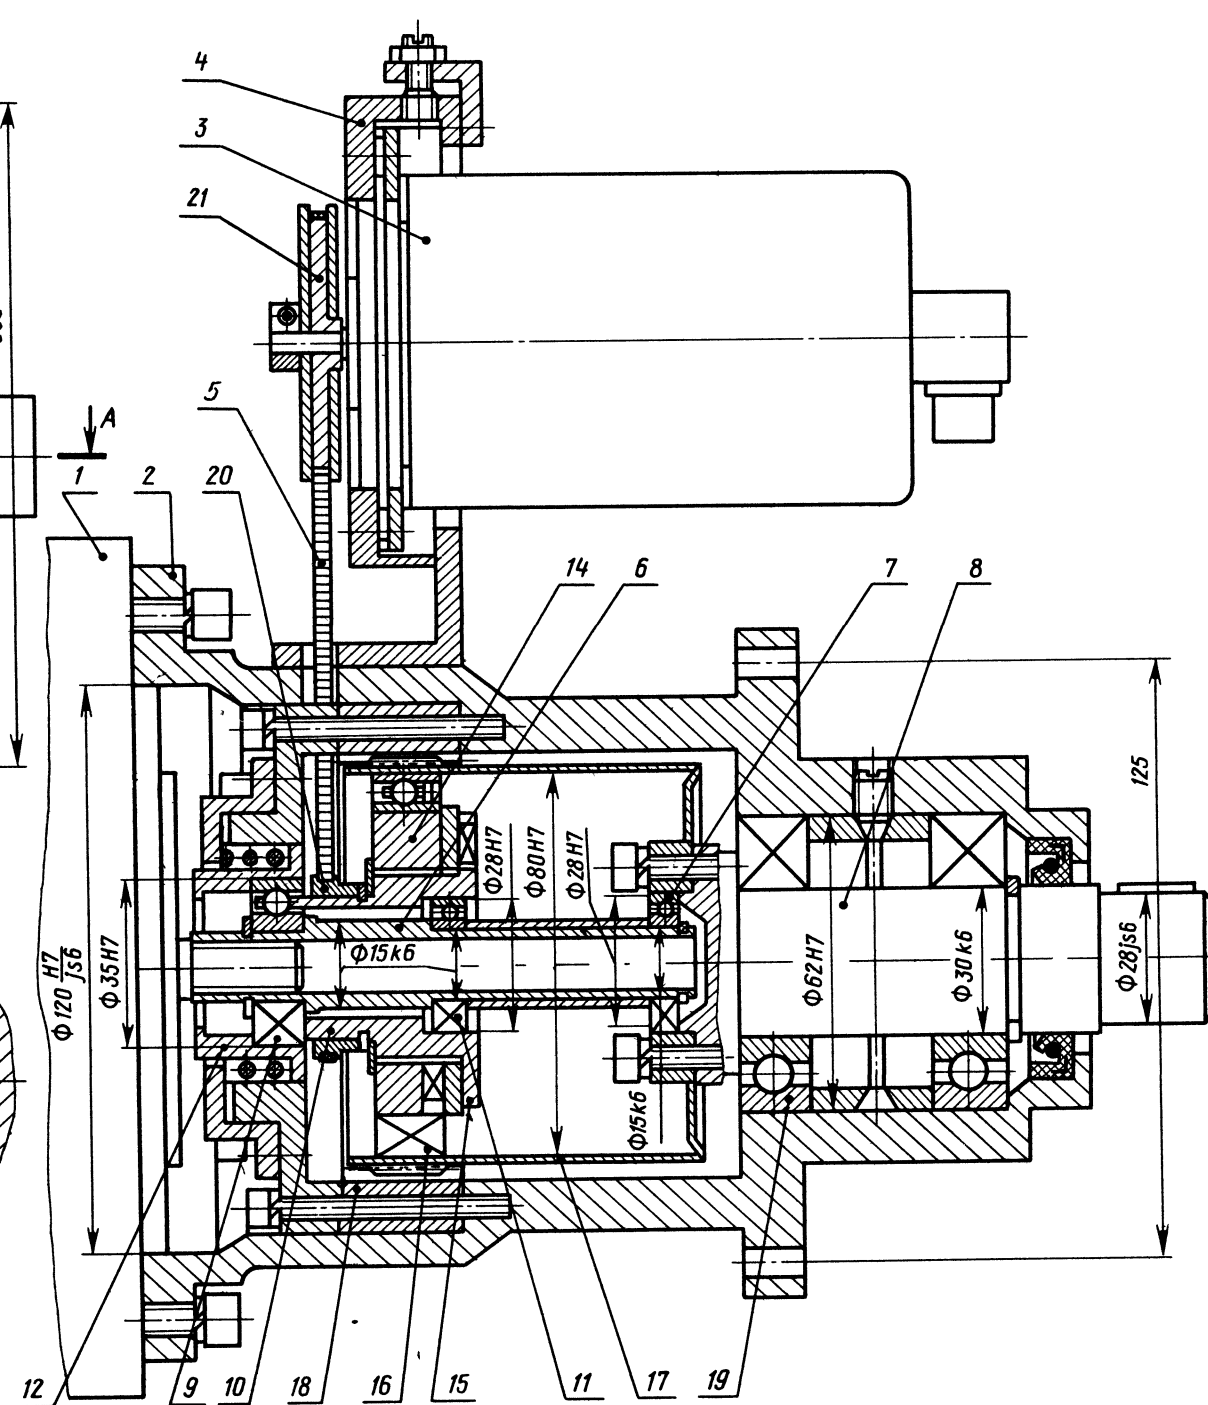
Механизм привода поворота руки для ПР типа ПР-4
